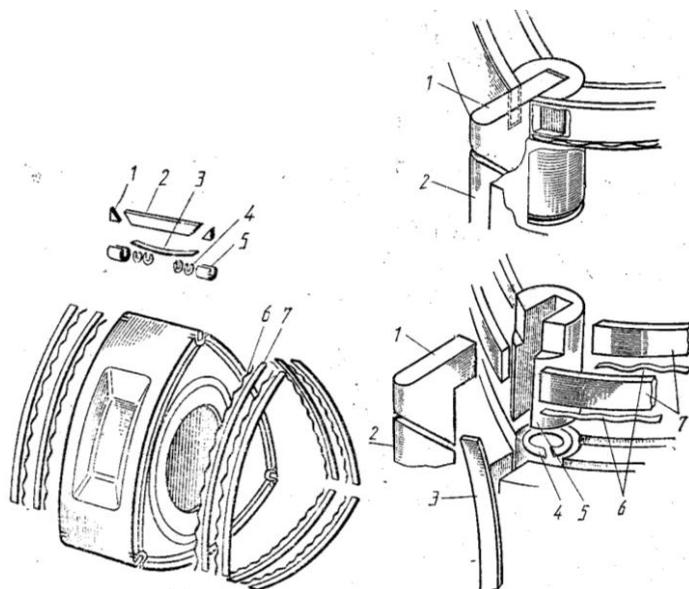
Уплотнения ротора роторно-поршневого двигателя:
